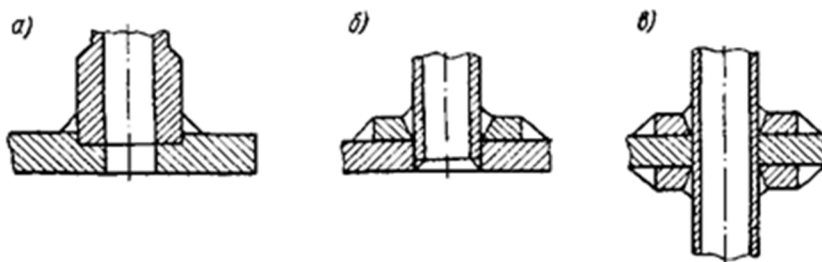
Схемы усиления отверстий: а – патрубком, б – патрубком и накладкой, в – патрубком и двумя накладками
